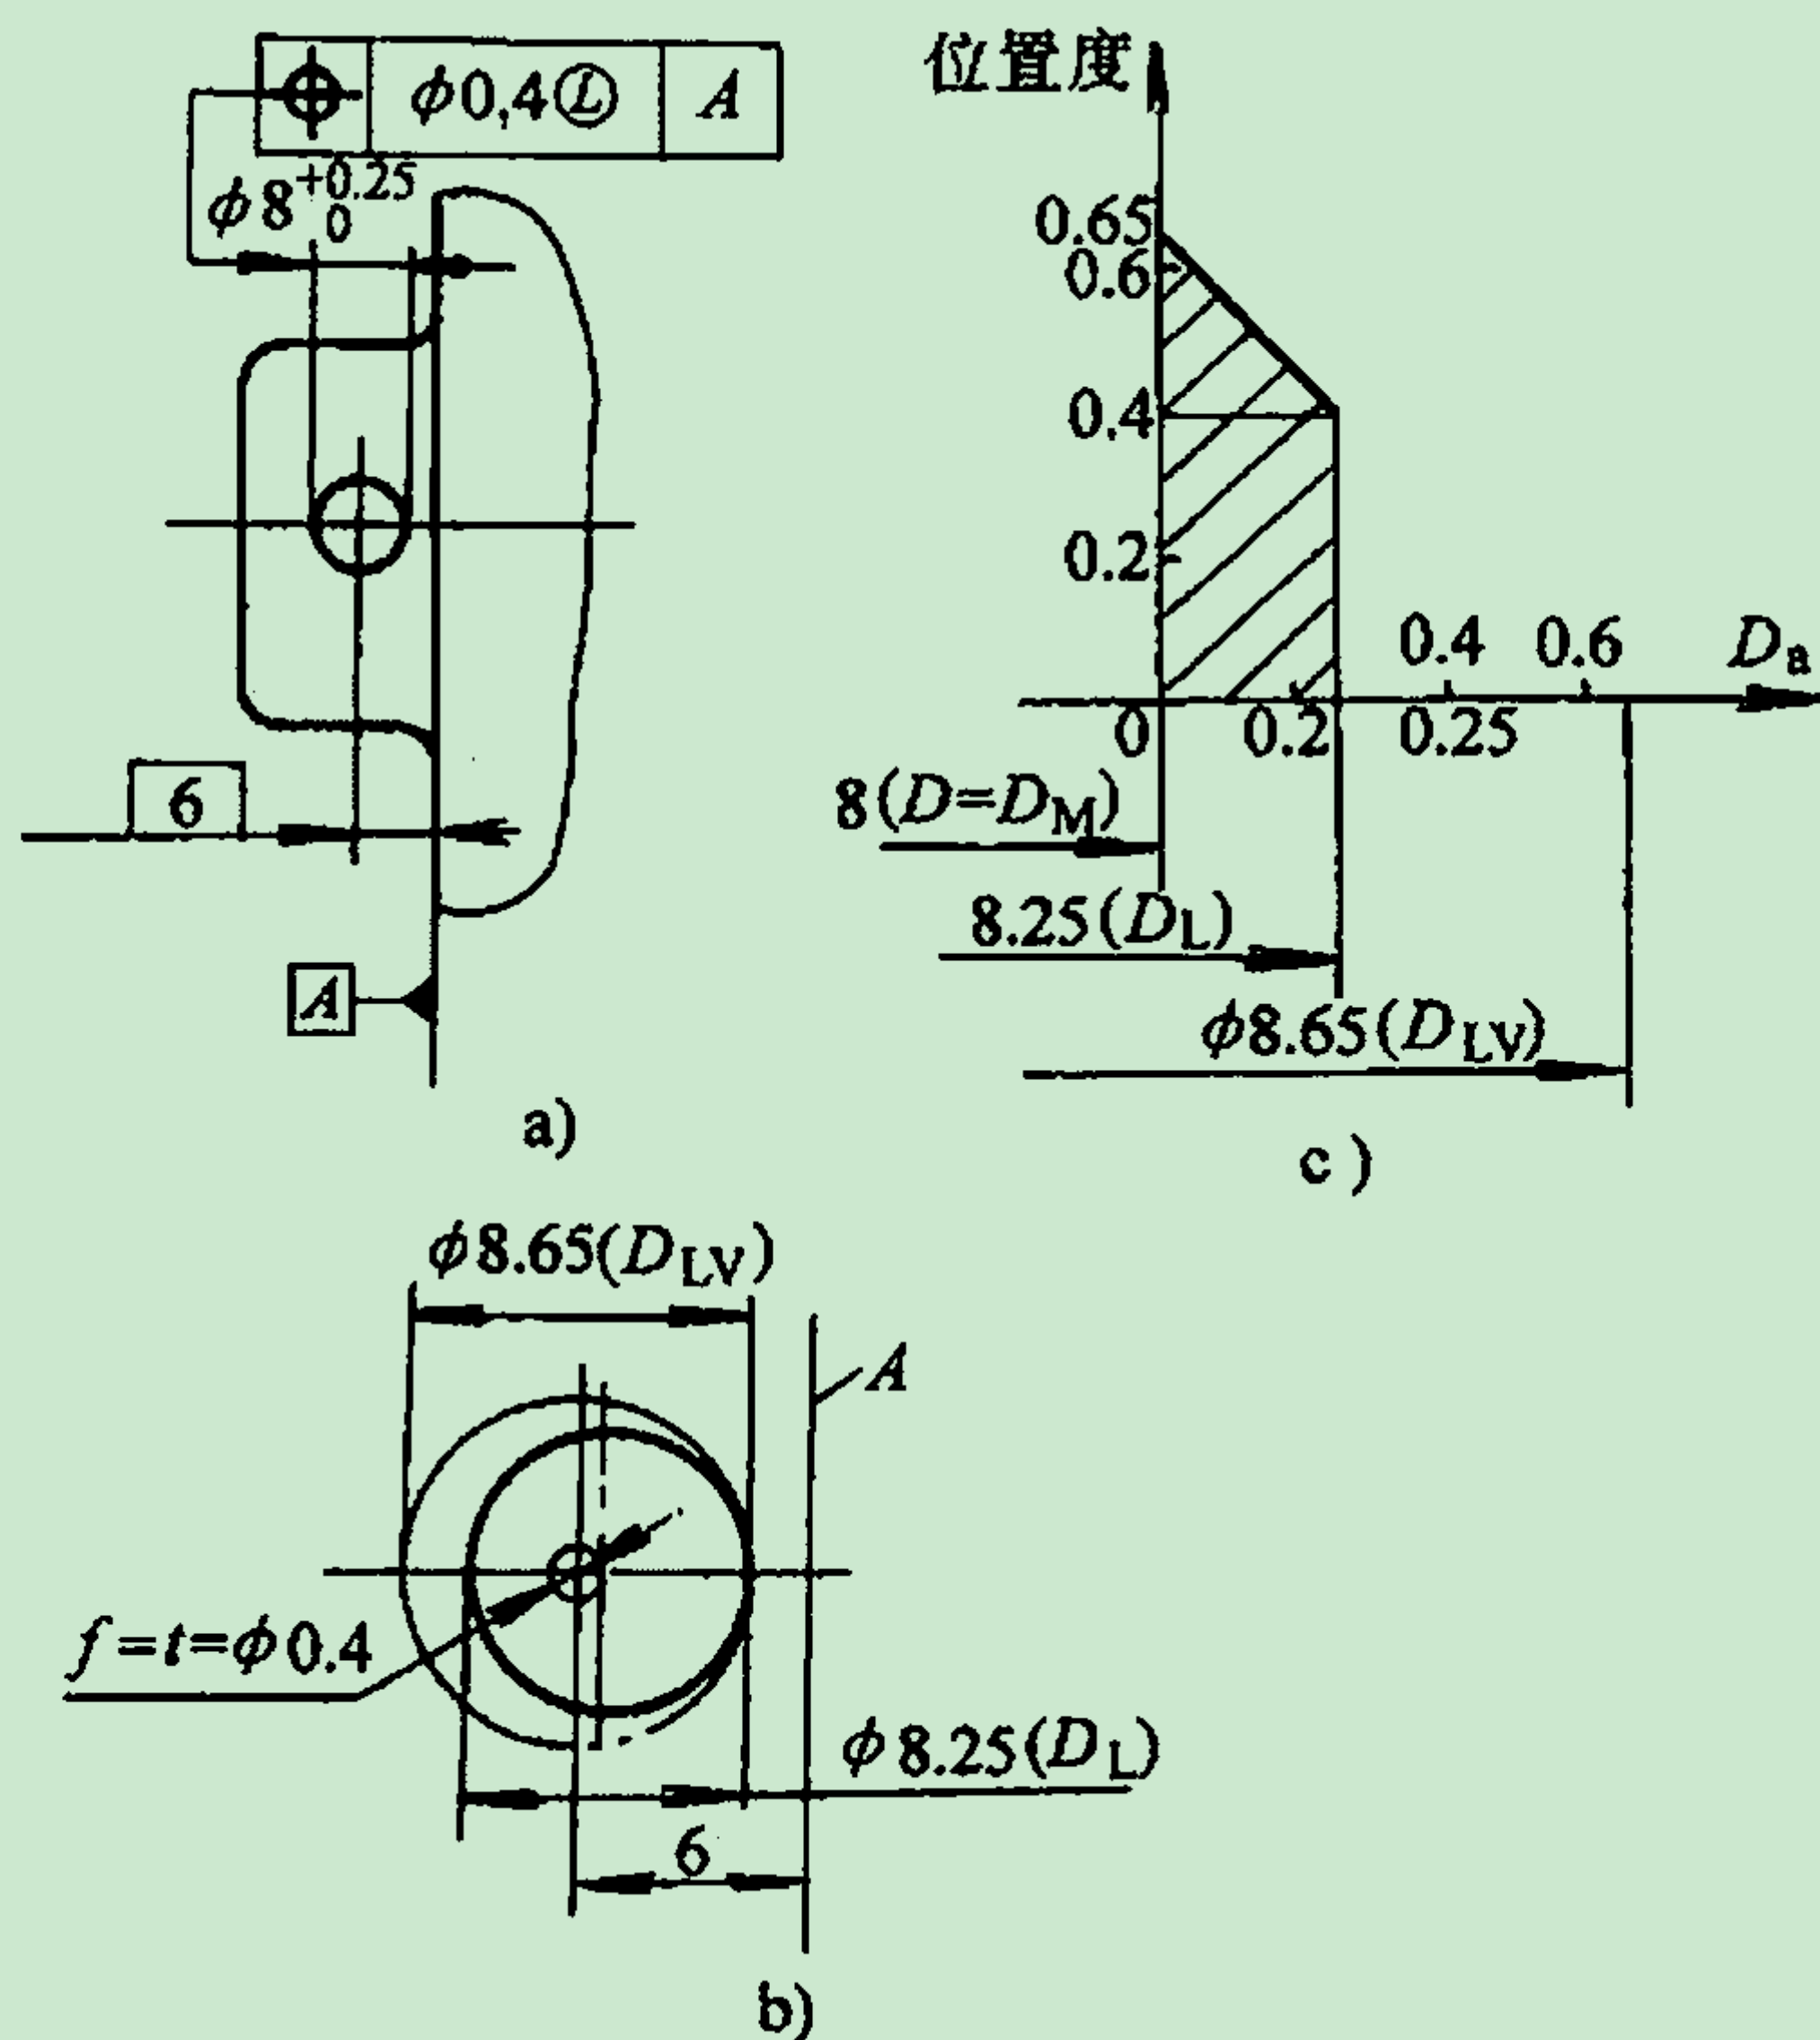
轴线位置度公差采用最小实体要求
